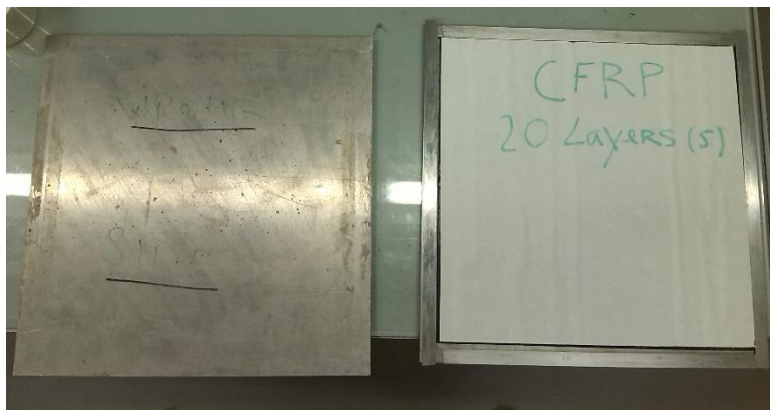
Posicionamento da placa de carbono-epóxico no molde
